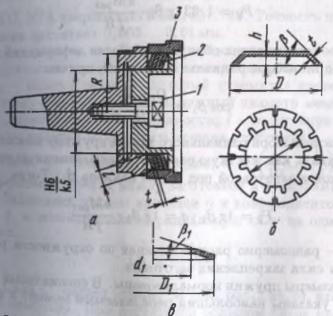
Разжимная оправка с тарельчатыми пружинами (a), тарельчатая пружина в свободном состоянии (б) и после выбора зазора (в)
